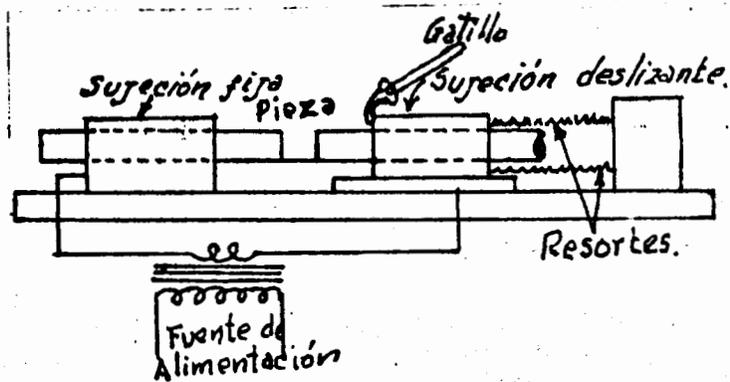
ESQUEMA DEL PROCESO DE SOLDADURA POR PERCUSIÓN.
